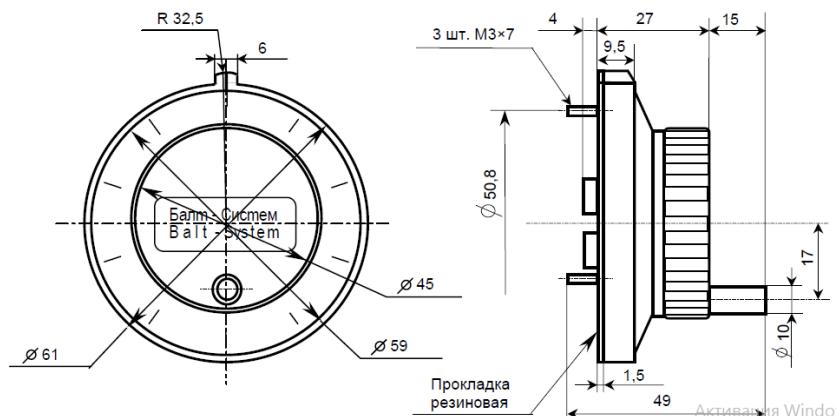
Габаритные размеры штурвала ZBG-5-003-100
